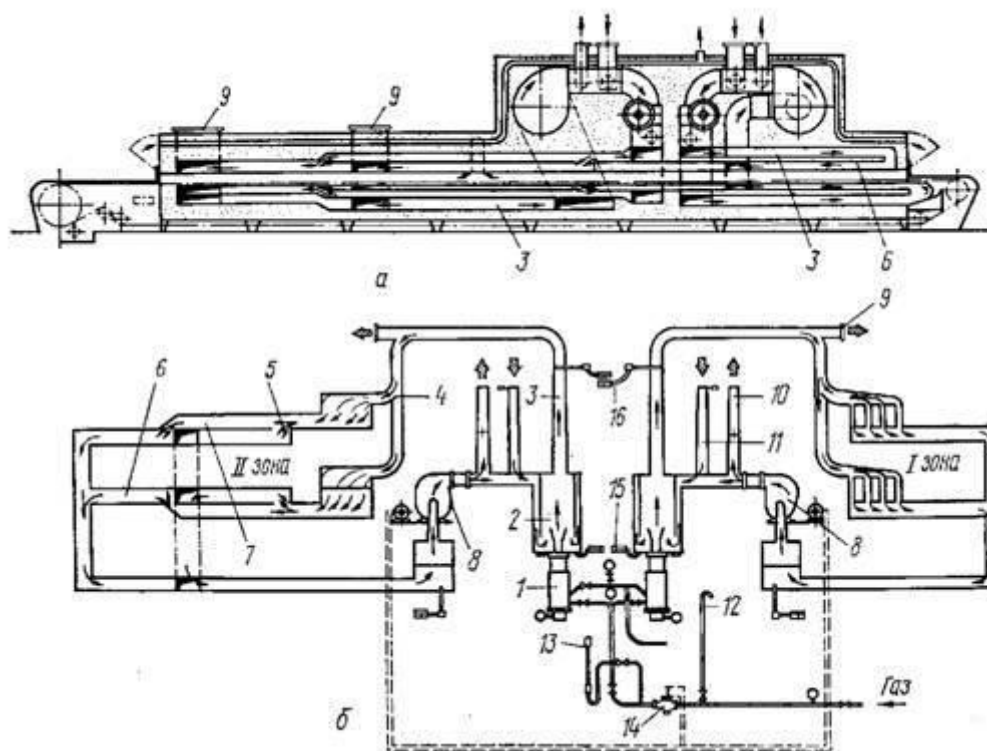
Піч ПХС-25: а - поздовжній розріз; б - схема газорозподілу); 1 - пальник з розведенням газу; 2-топка зі змішувальною камерою; 3 - транспортують канали; 4 - інсталяційний клапан; 5 - зональний клапан; 6 - робочі канали; 7 - транзитні канали; 8 - димососним агрегат; 9 - противибухові клапани; 10 - патрубок для газів, що йдуть; 11 - патрубок для продувки ogrівальної системи; 12 - продувальна свічка; 13 - переносний запальник; 14 - електромагнітний клапан-відсікач; 15 - тягоміри; 16 - термопара з мілівольтметром
